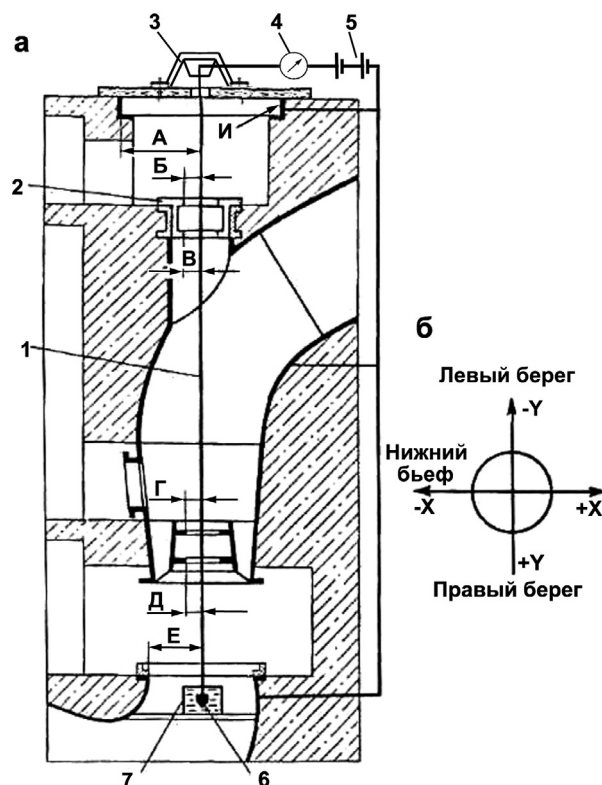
Схема центровки корпусных частей осевого вертикального насоса:
